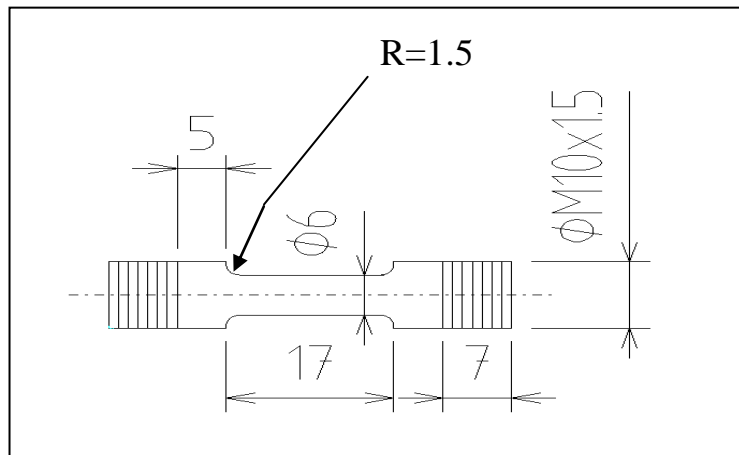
Géométrie des éprouvettes transverses (dimensions en mm)
